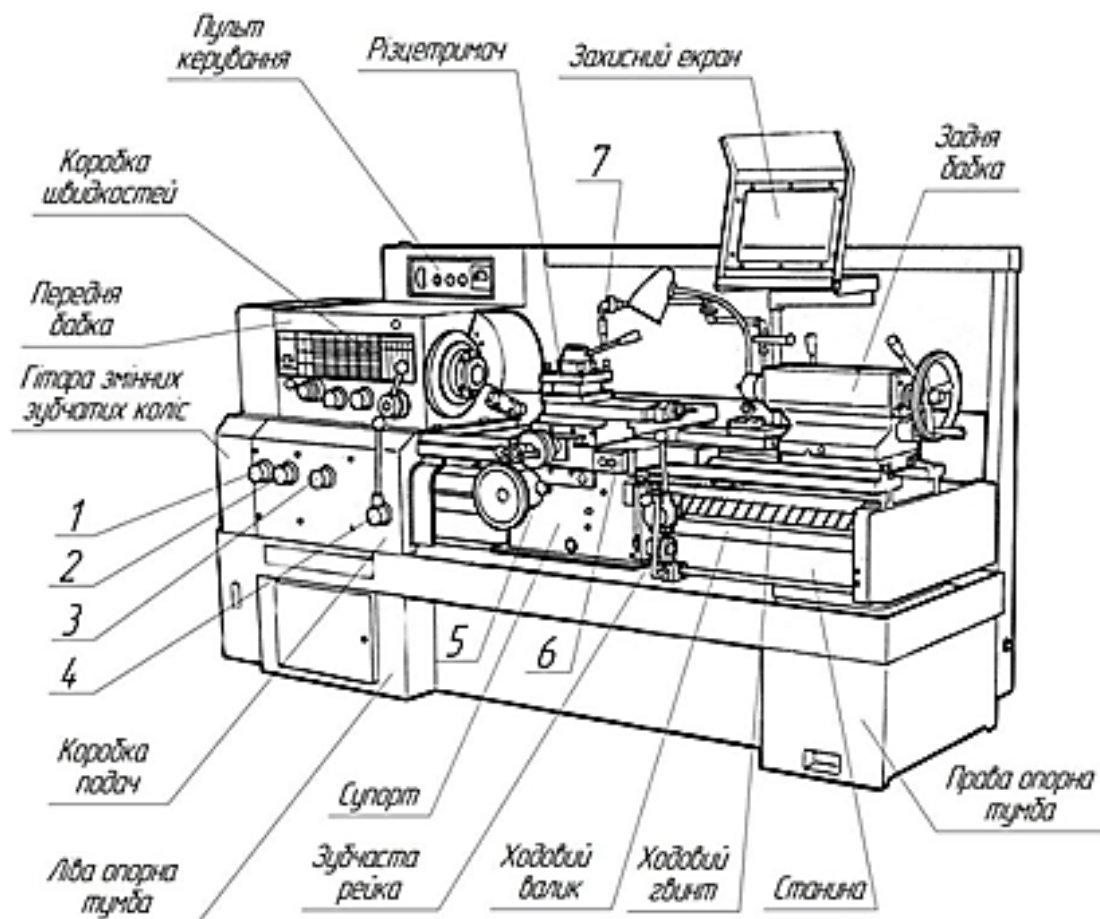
Будова токарно-гвинторізного верстату 16К20 (1,2,3 – ручки управління коробкою подач, 4 – ручка включення обертання шпинделя, 5 – маховичок повздовжнього переміщення супорта, 6 – кнопка включення електродвигуна верстата, 7 – подача охолоджуючої рідини)
